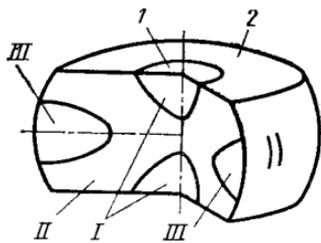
Зоны деформации при осадке цилиндрической заготовки
